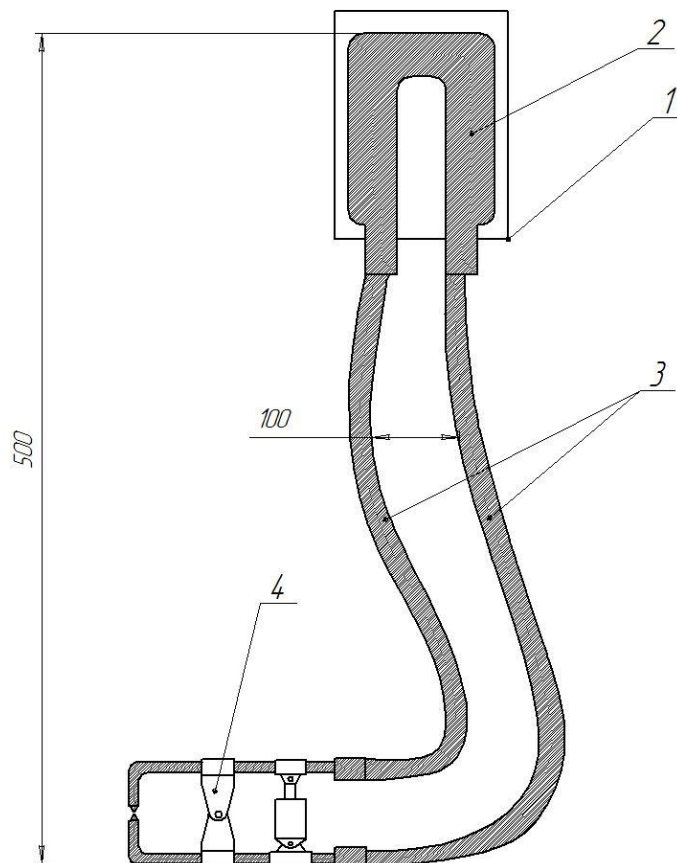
Электрическая схема сварочного контура
